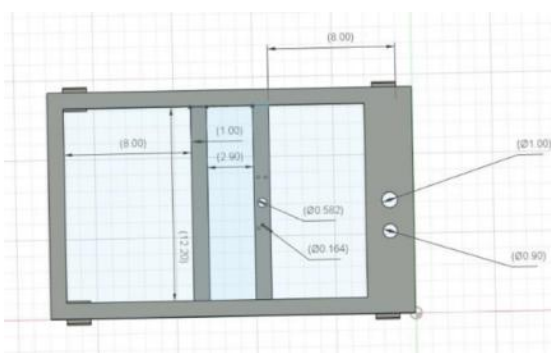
Конструкція шасі з розмірами (вид зверху)
